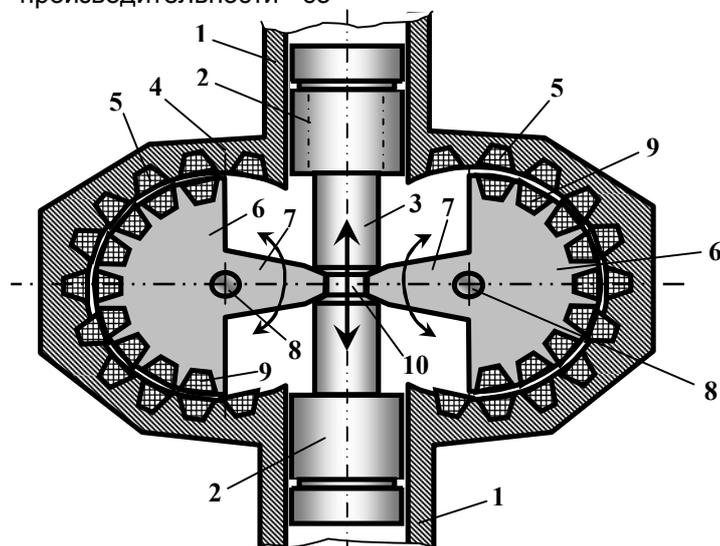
Конструктивная схема оппозитного компрессора с двухвальным электромагнитным приводом: 1. Цилиндр. 2. Поршень 3. Общий шток. 4. Корпус. 5. Обмотка статора. 6. Якорь. 7. Выступ. 8. Неподвижная ось. 9. Обмотка якоря. 10. Впадина
